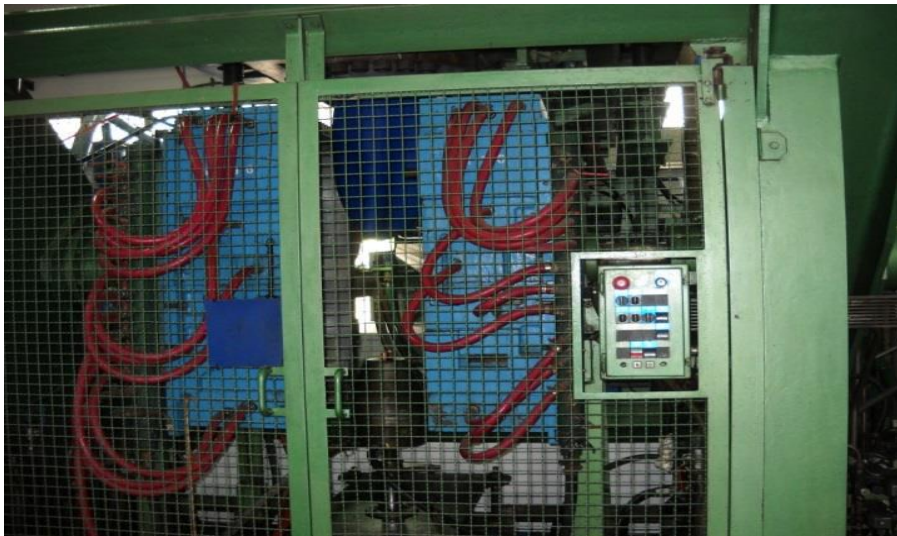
fuente propia. Proceso de apertura de molde y expulsión
